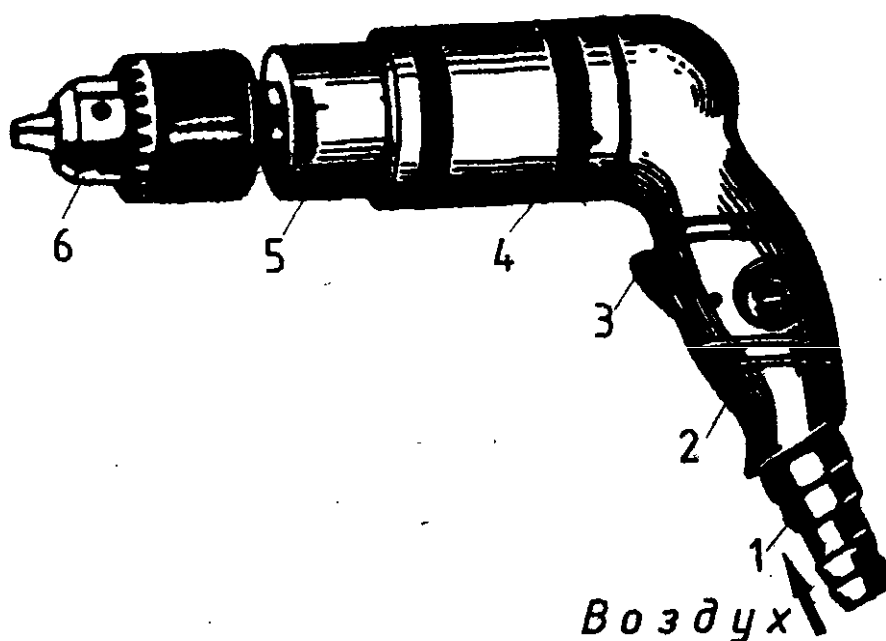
Ручная сверлильная пневматическая машина Д-2:
